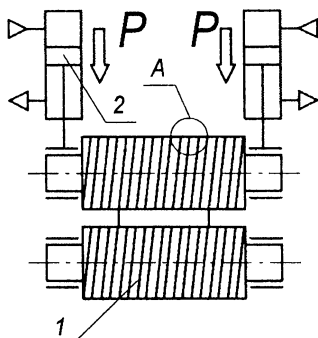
Схема стана для поверхностного упрочнения рессорных листов
